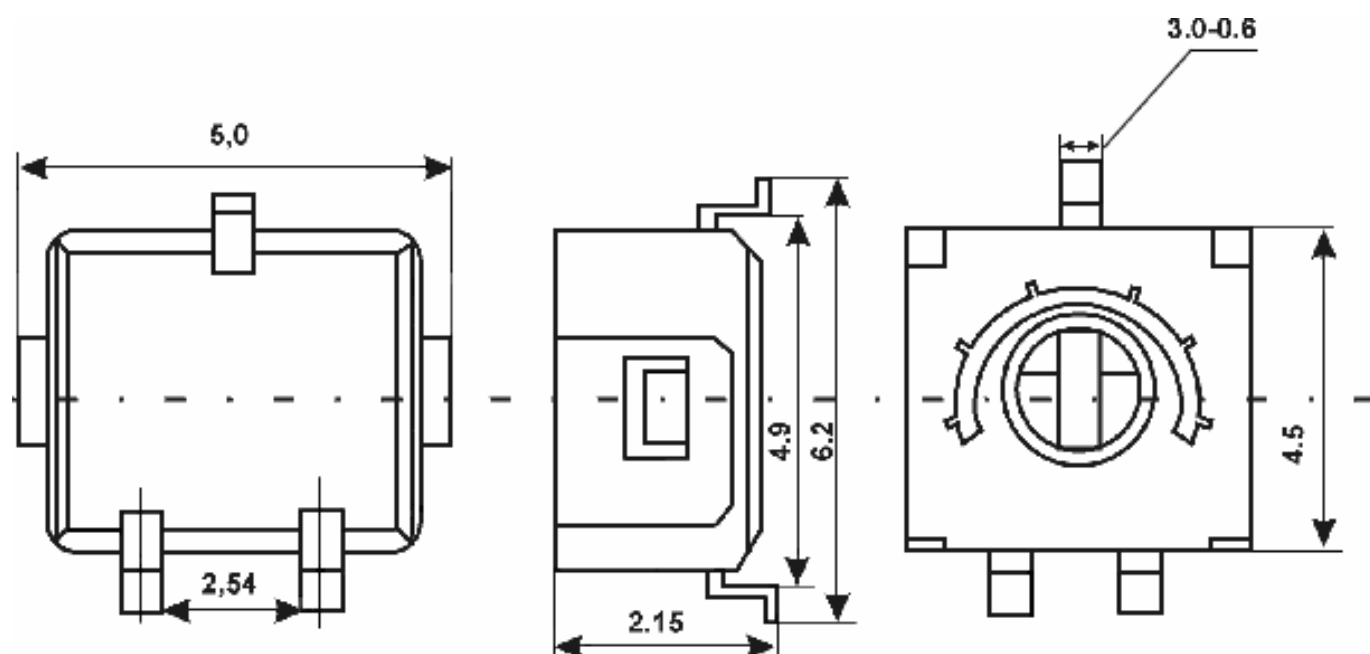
Конструкция, габаритные и присоединительные размеры корпусов ST-4B. Размер шлица - 3,2 (длина); 0,6 (ширина); 0,5 - глубина
